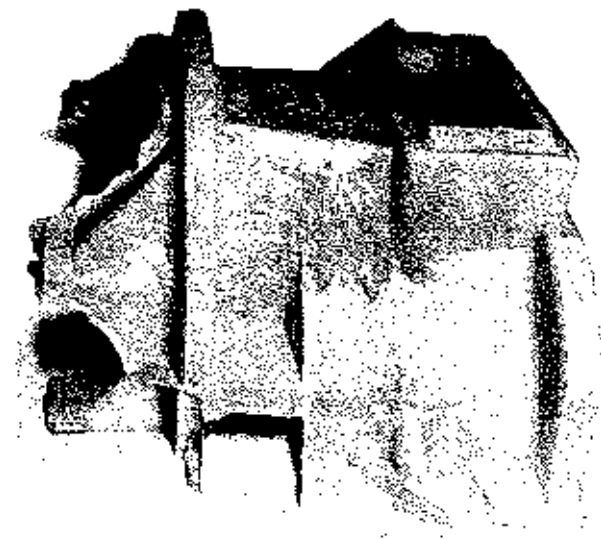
Defecto típico de penetración metálica en fundición laminar debida a explosión en los moldes.
